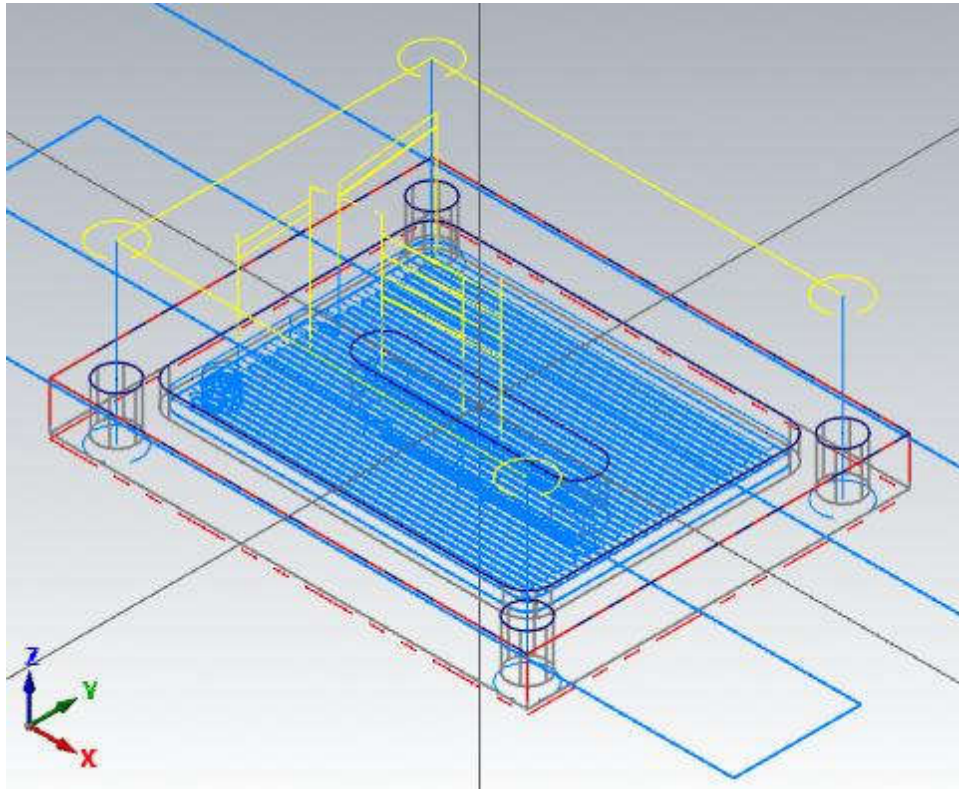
Présentation des cinq stratégies d'usinage ensemble
